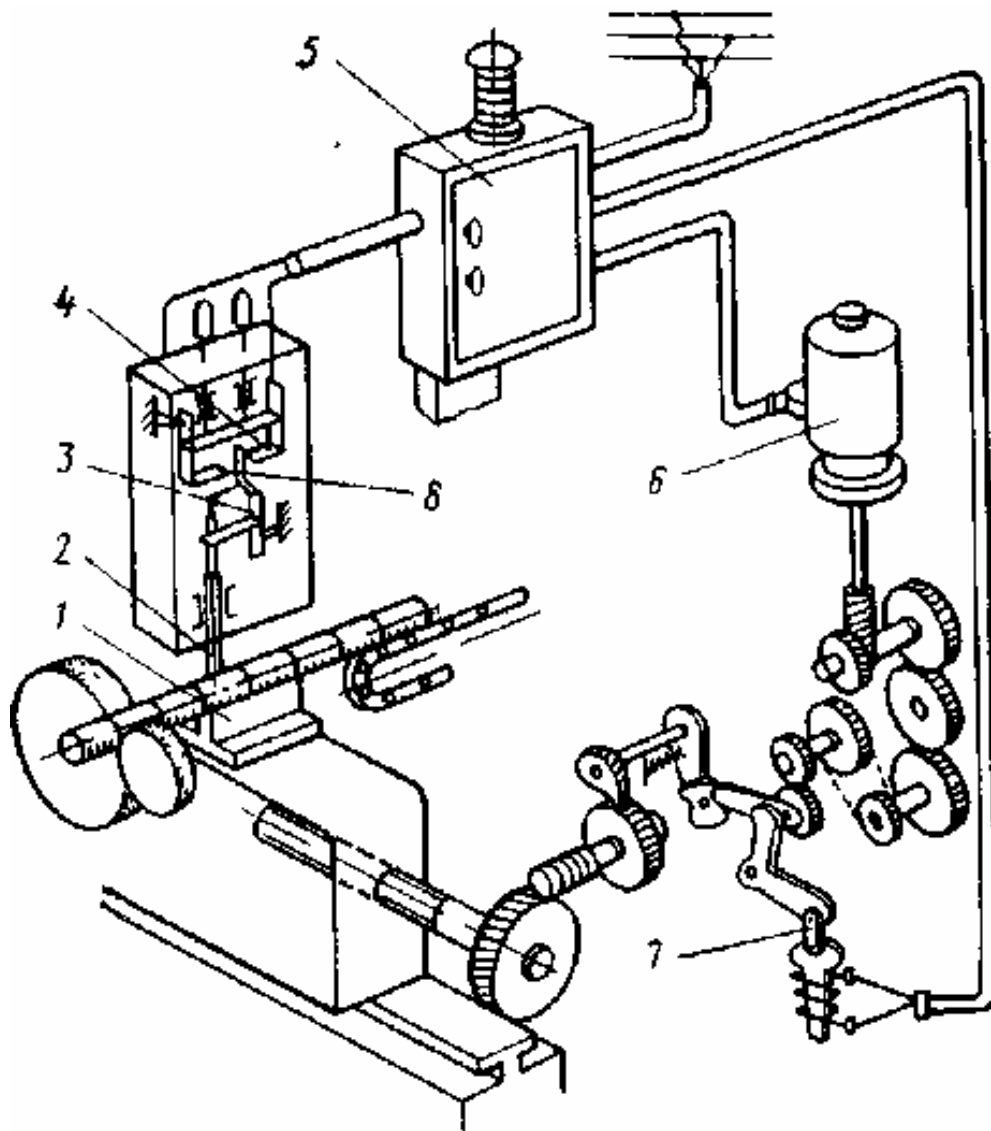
Пристрій для автоматичної піднастройки безцентрово-шліфувального верстата
